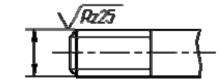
Пример обозначения шероховатости наружной резьбы
